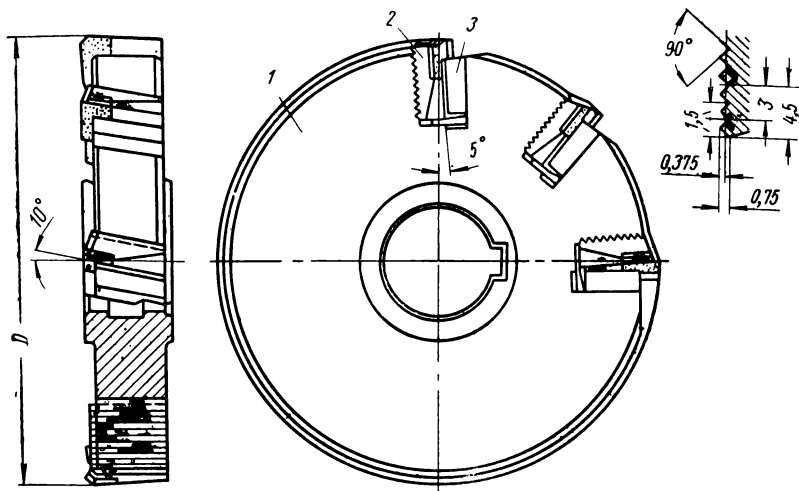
Крепление клином плоских ножей с рифлями в корпусе дисковой фрезы (конструкция по ГОСТам 5348—60 и 6469—60):
